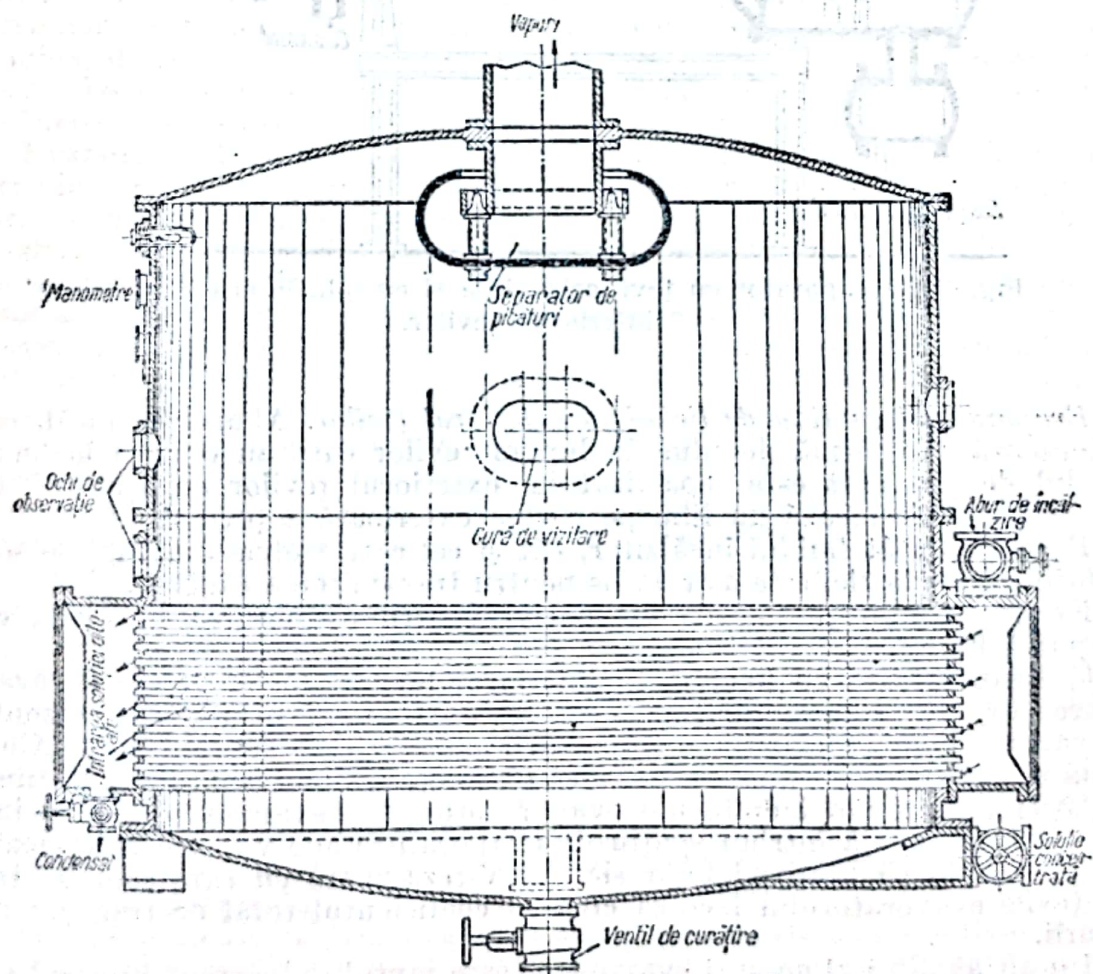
Evaporator cu țevi orizontale și cu soluția circulând în exteriorul țevelor.
